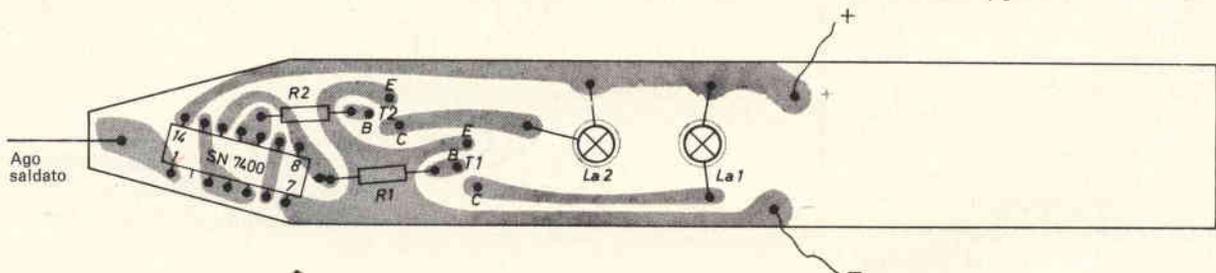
Assemblaggio dei componenti dell'indicatore L-H per frequenze di impulsi rettangolari sino a 30 MHz.
